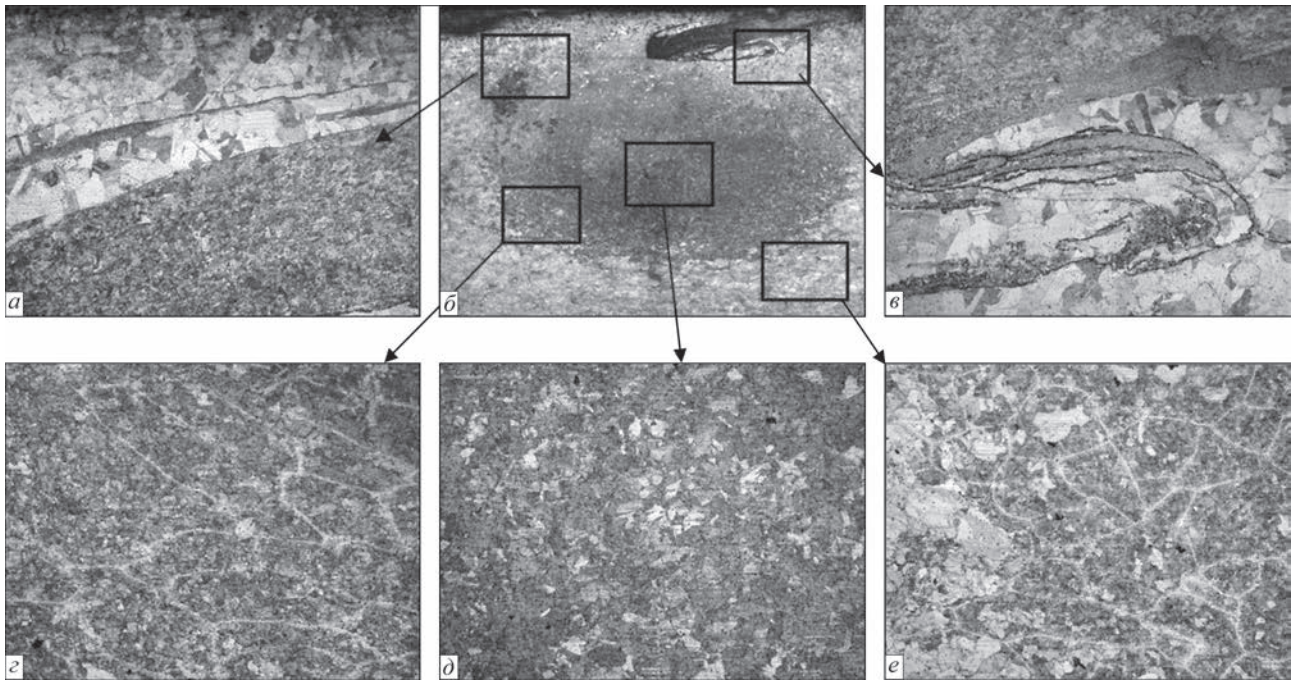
Мікроструктура зварного з'єднання зразка № 1: верхня частина шва (а, в), загальний вигляд (б), зона ядра (д), ЗТМВ (г), ЗТВ (е); б – $\times 25$; а, в–е $\times 100$, травлено
